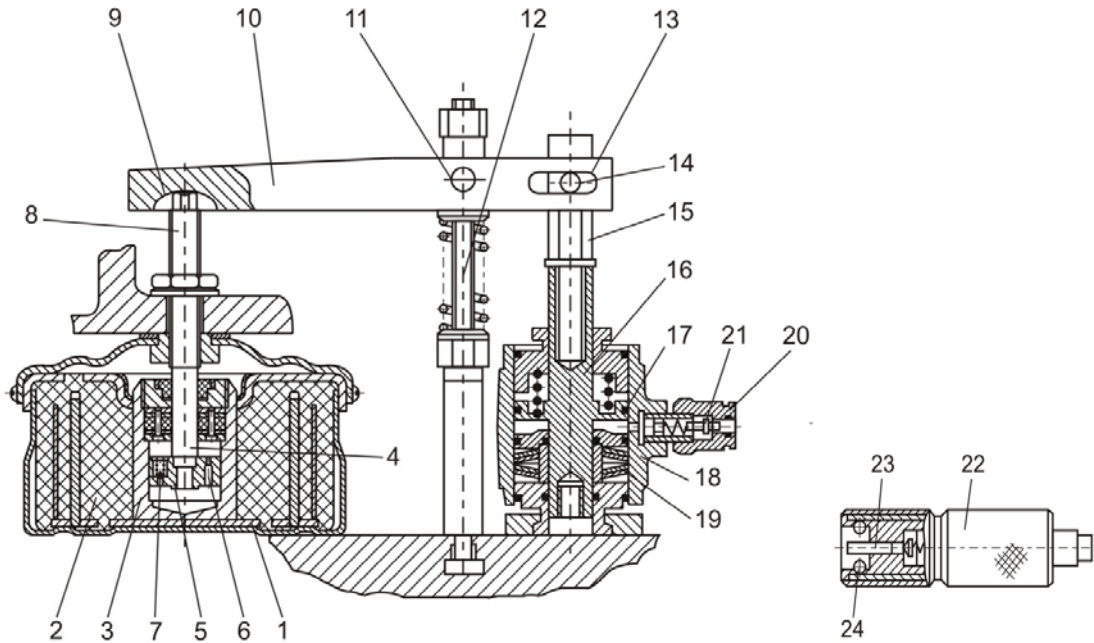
Общий вид виброизолирующего устройства: 1 – основание; 2 – резиновый элемент; 3 – цилиндр; 4 – шток; 5 – поршень; 6 – калиброванное отверстие; 7 – клапан сжатия; 8 – регулировочный винт; 9 – сферическая поверхность лунки; 10 – прихват; 11 – ось; 12 – стойка; 13 – продольный паз; 14 – ось; 15 – опора; 16 – опорный шток; 17 – поршень; 18 – гидроцилиндр; 19 – пружинный аккумулятор; 20 – малая полумуфта; 21 – клапан; 22 – большая полумуфта; 23 – клапанный штырь; 24 – шарики.
